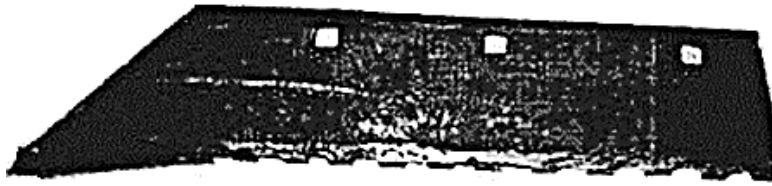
Загальний вигляд наплавленого леміша [14]
